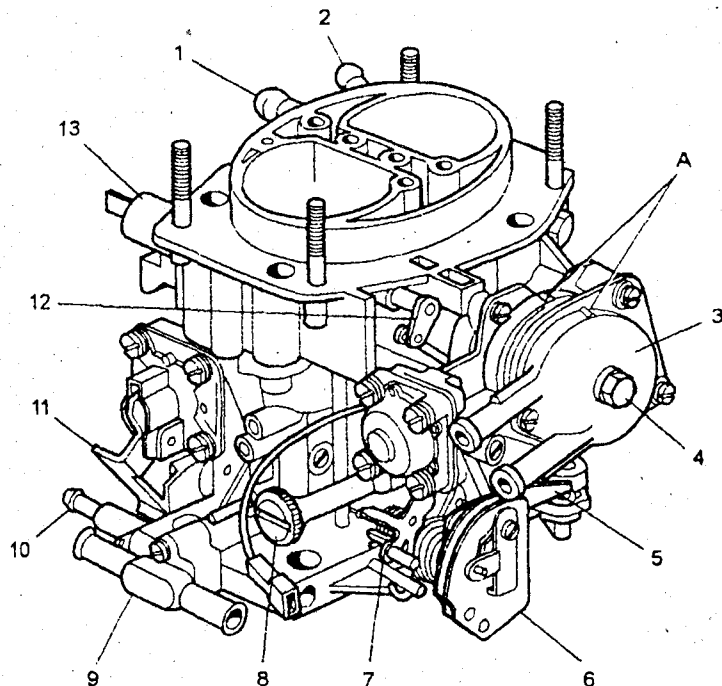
Внешний вид карбюратора 21081-1107010-31: 1 – патрубок подачи топлива от топливного насоса; 2 – патрубок слива части топлива в топливный бак (“обратка”); 3 – корпус жидкостной камеры; 4 – болт крепления жидкостной камеры; 5 – рычаг дроссельной заслонки; 6 – сектор рычага управления дроссельными заслонками; 7 – ведущий рычаг привода второй камеры; 8 – регулировочный винт количества смеси холостого хода; 9 – блок подогрева карбюратора; 10 – патрубок вентиляции картера двигателя; 11 – рычаг привода ускорительного насоса; 12 – рычаг воздушной заслонки; 13 – электромагнитный запорный клапан
